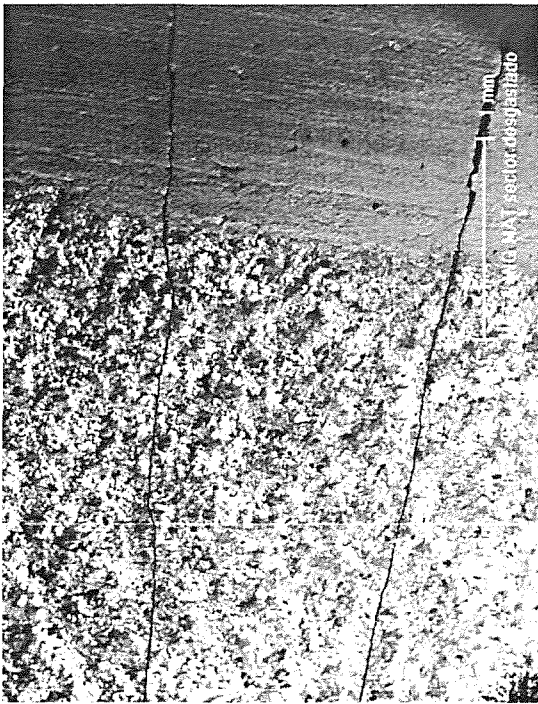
Grietas que atraviesan totalmente un sector del forro.
